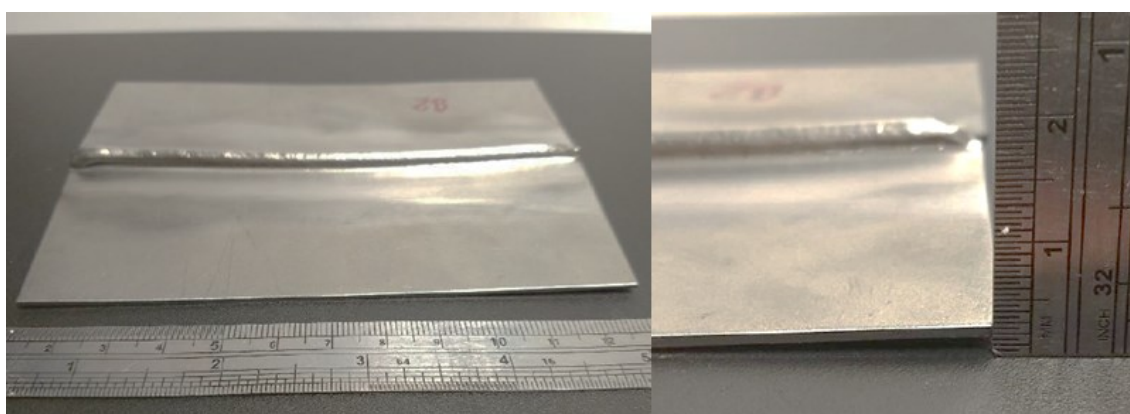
Cordão em passe único e contínuo, condição de soldagem 2 com empenamento da chapa. (Próprio autor)
